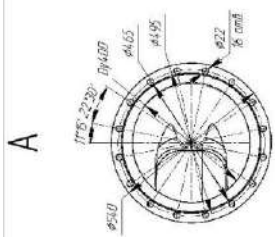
Габаритные и присоединительные размеры НФ2 400/750.748-6.315/8-400
